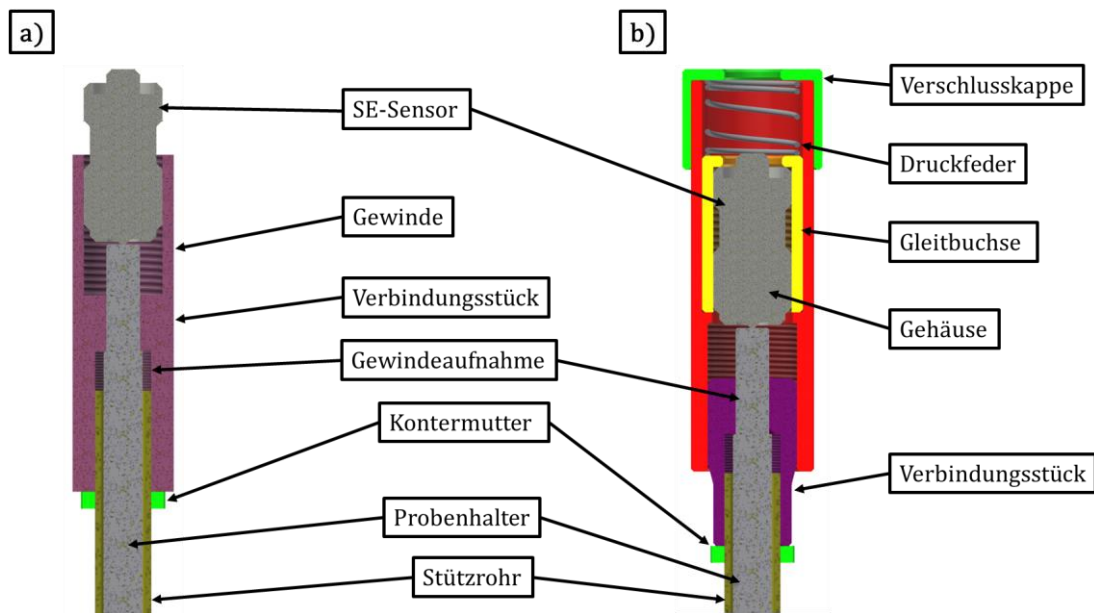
Anbringung des SE-Sensors wie gehabt mittels Gewinde (links) und mittels der neu entwickelten, federgespannten Ausführung (rechts).
